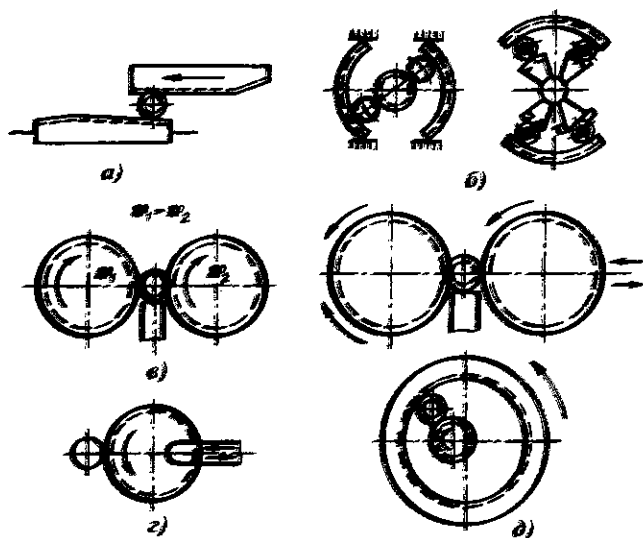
Схемы накатывания наружных резьбовых поверхностей:
